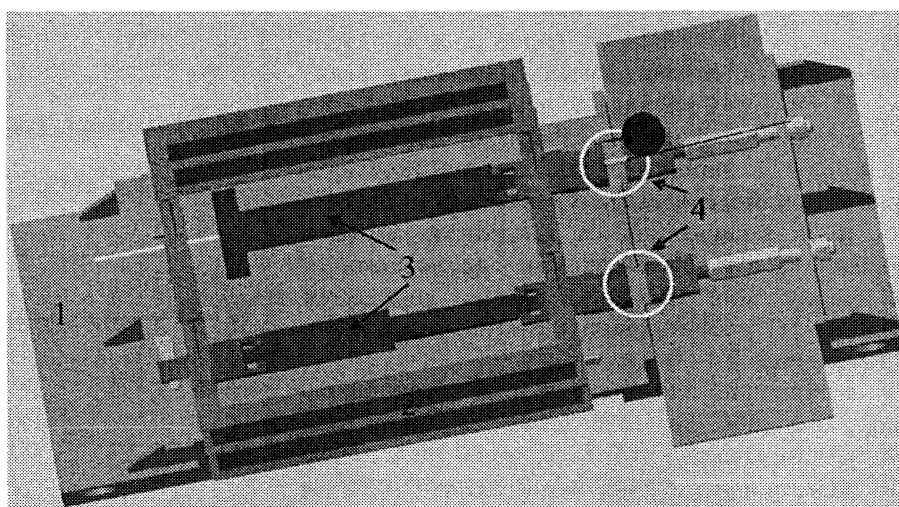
Экспериментальная установка для изучения силового взаимодействия формы и металла отливки в период затвердевания
